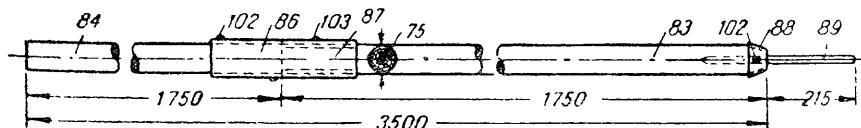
Средняя стойка: 83 — верхняя часть древка; 84 — нижняя часть древка; 86 — соединительная муфта; 87 — гильза; 85 — колышь; 89 — штырь; 102 — шуруп полукруглый; 103 — гвоздь
